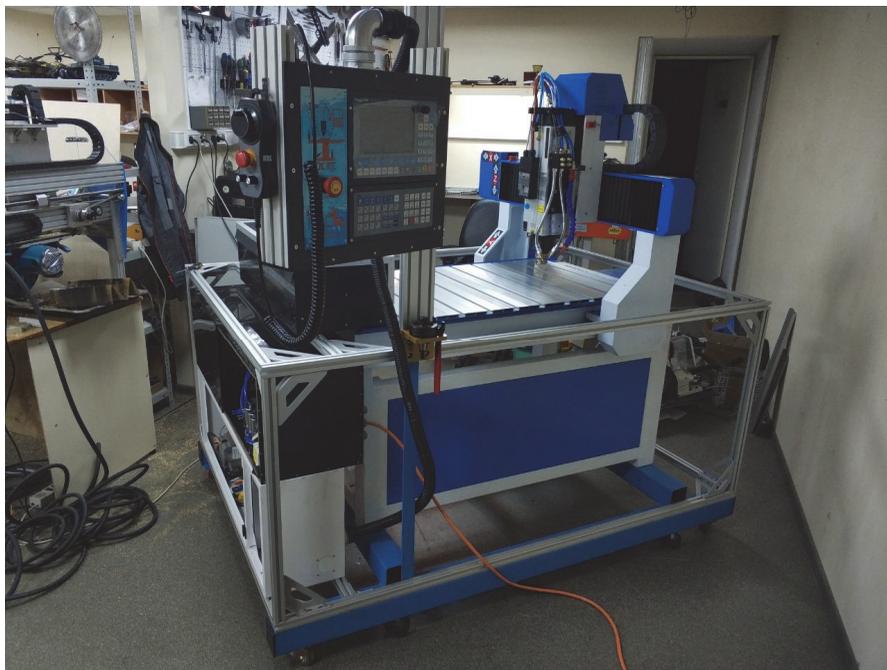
Фрезерный ЧПУ станок с автоматической сменой инструмента
